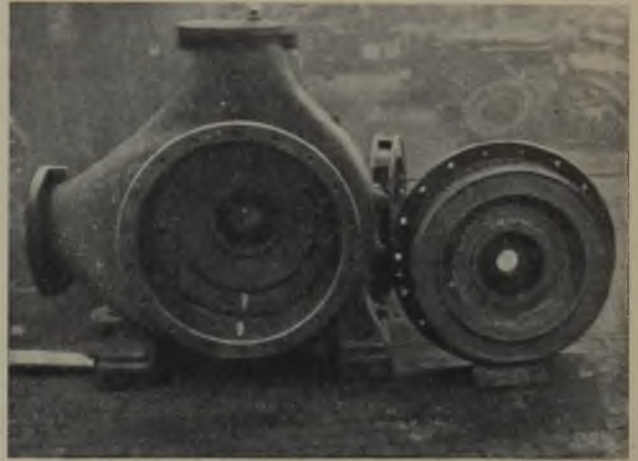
Aufgeschweißtes Pumpengehäuse.
